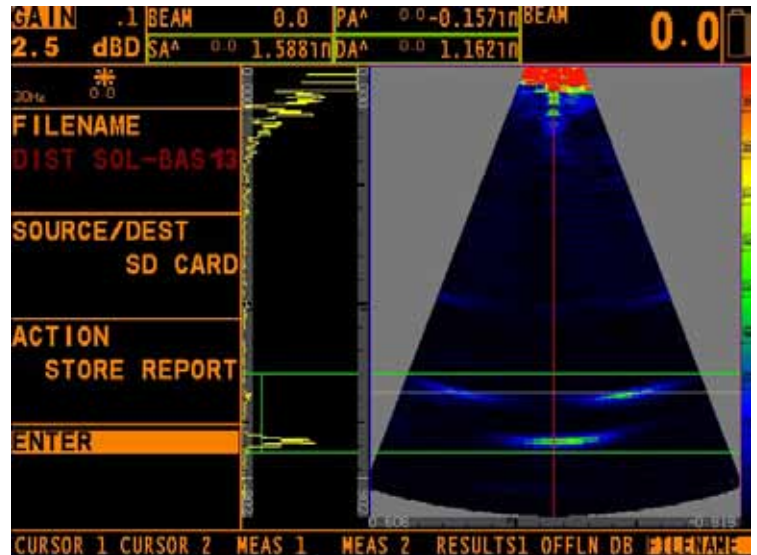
Imagen del Barrido Sectorial a 0°, tocando parte de la corona de la soldadura.
